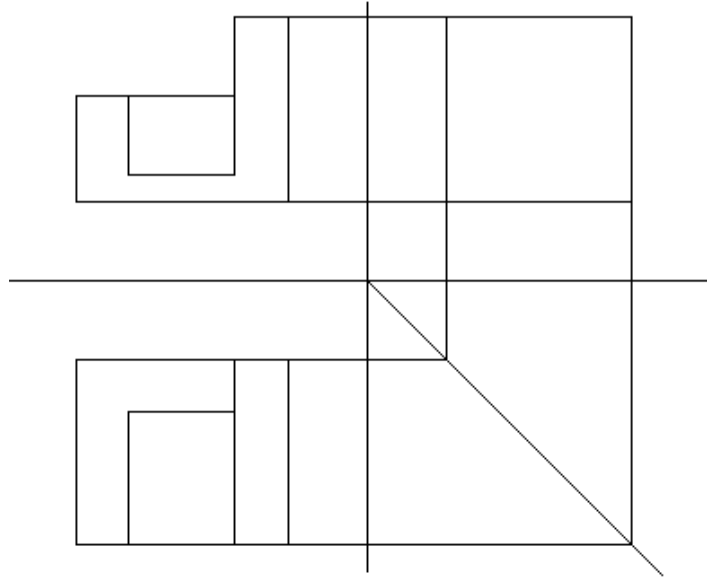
Temel boyutların yatay düzleme taşınması
